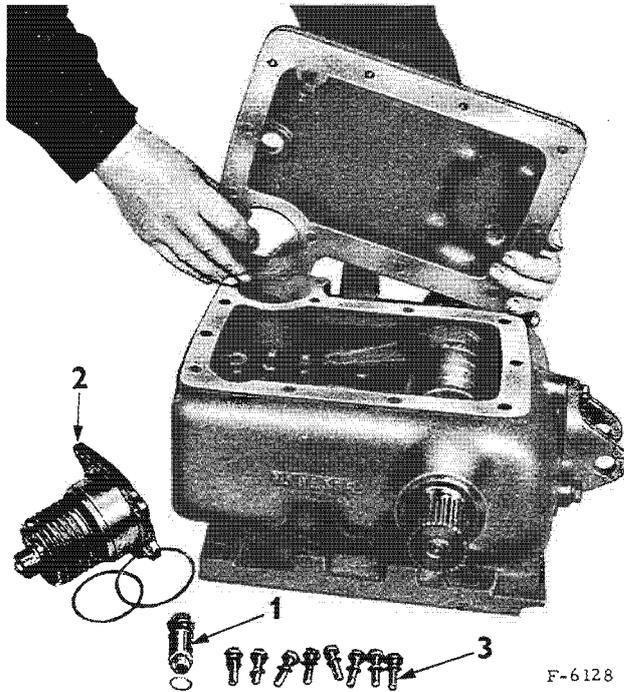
Démontage du couvercle du relevage des 135. Ordre de démontage : 1. Cheminée sur le couvercle; 2. Vis du filtre et filtre; 3. Vis de fixation du couvercle
